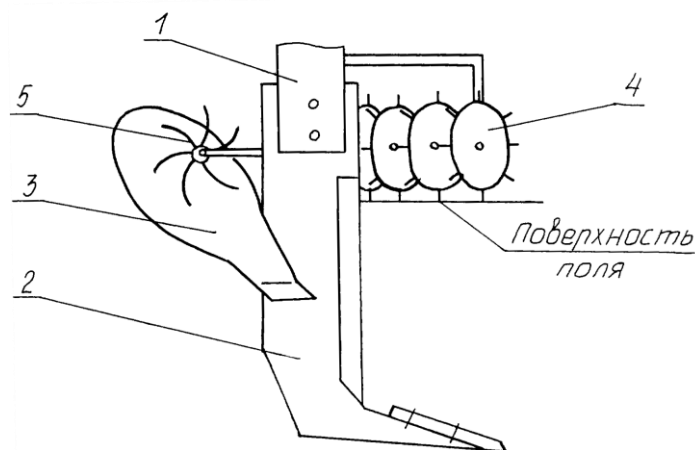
Однооперационный агрегат с вычесывающим направителем: 1 – рама; 2 – щелерез; 3 – отвал; 4 – сгребующее приспособление; 5 – соломонабиватель
